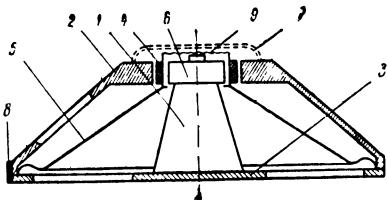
Конструктивный чертеж громкоговорителя: 1 — магнит, 2 — конусообразная чашка, 3 — экран-ирующий диск, 4 — звуковая катушка, 5 — диффузор, 6 — полюсный наконечник, 7 — защитный колпачок, 8 — бумажное кольцо, 9 — центрирующая шайба
